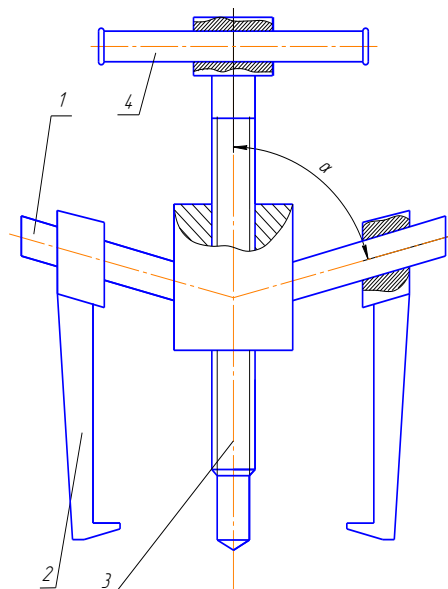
Общий вид съёмника: 1 – траверса; 2 – захваты; 3 – силовой винт; 4 – рычаг
